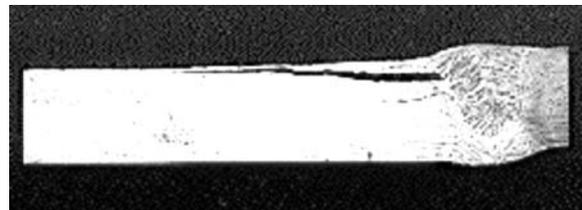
Элемент оболочки хранилища с расслоением металла у сварного шва
